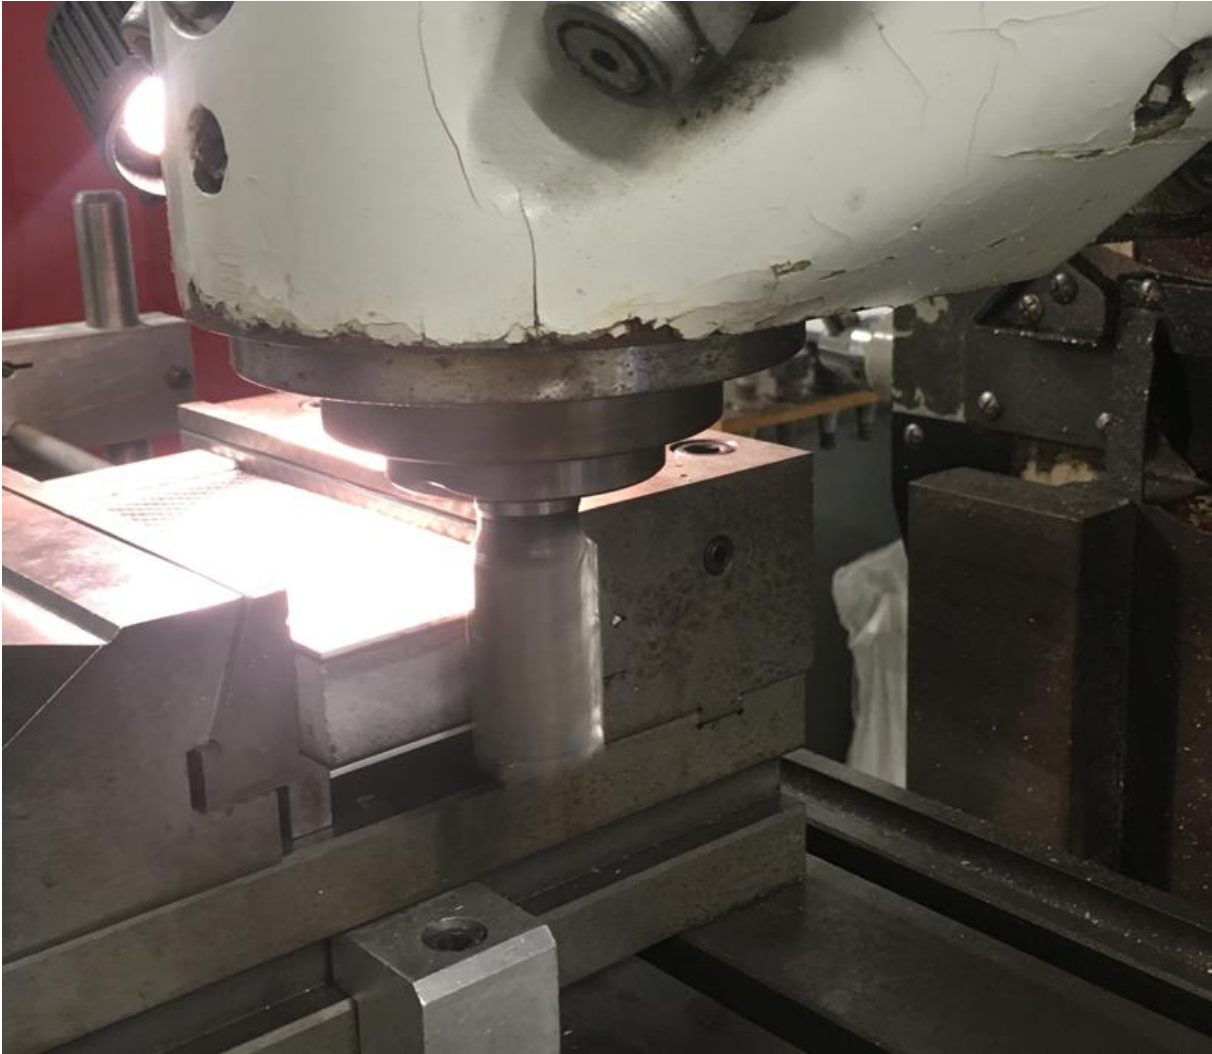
usinage des éprouvettes avec fraiseuse conventionnelle (fraise 2 tailles).
